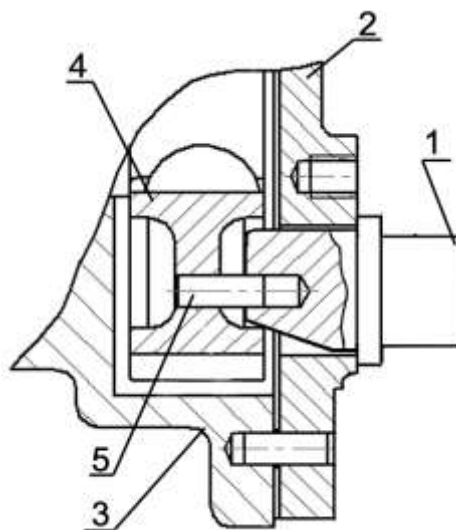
Фиксация шестерни редуктора: 1 – приспособление для фиксации установочного штифта; 2 – крышка редуктора; 3 - корпус редуктора; 4 – шестерня; 5 – штифт установочный
